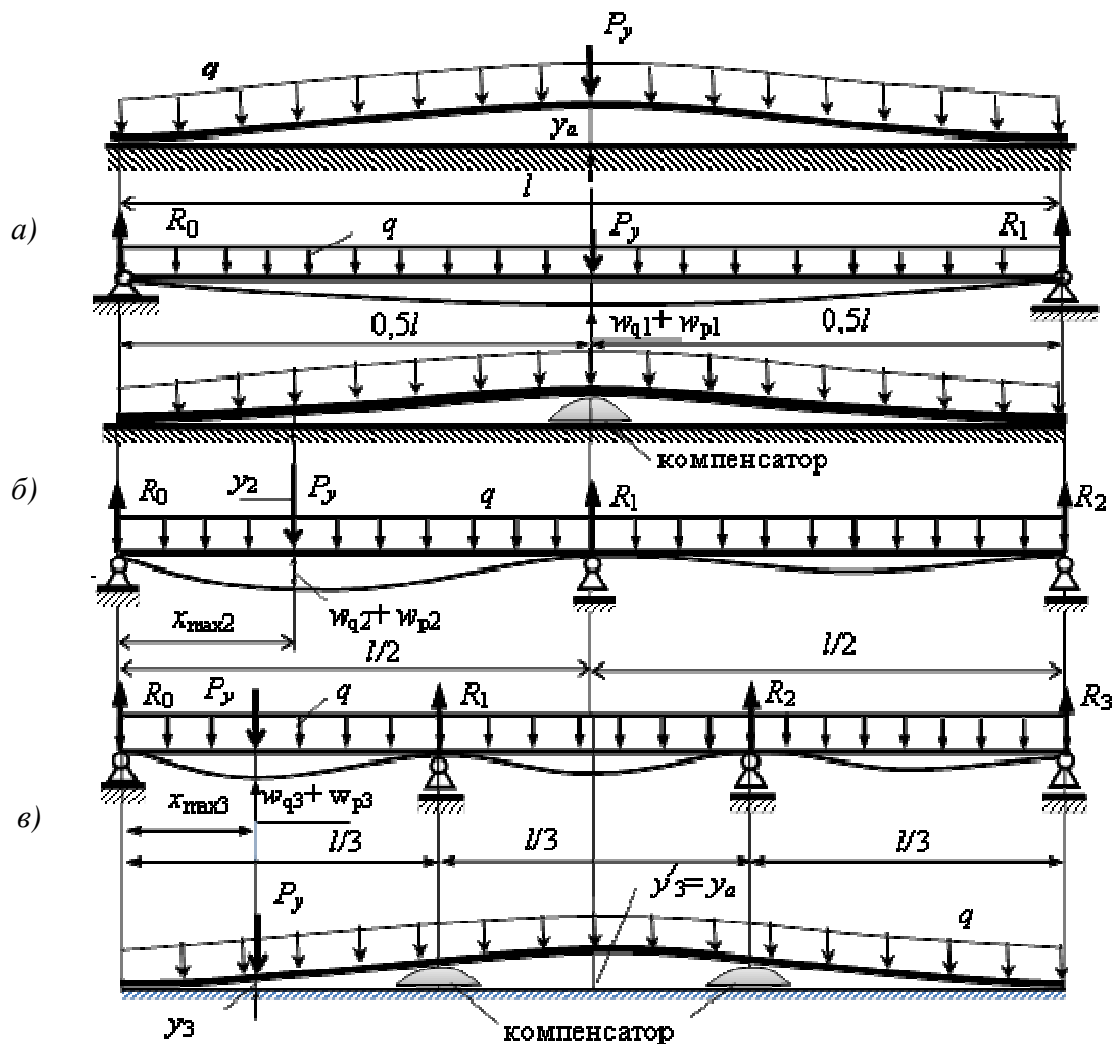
Расчетные схемы заготовки при шлифовании с закреплением магнитным полем стола: (а) - без компенсаторов, (б) – с одним компенсатором, (в) – с двумя компенсаторами
